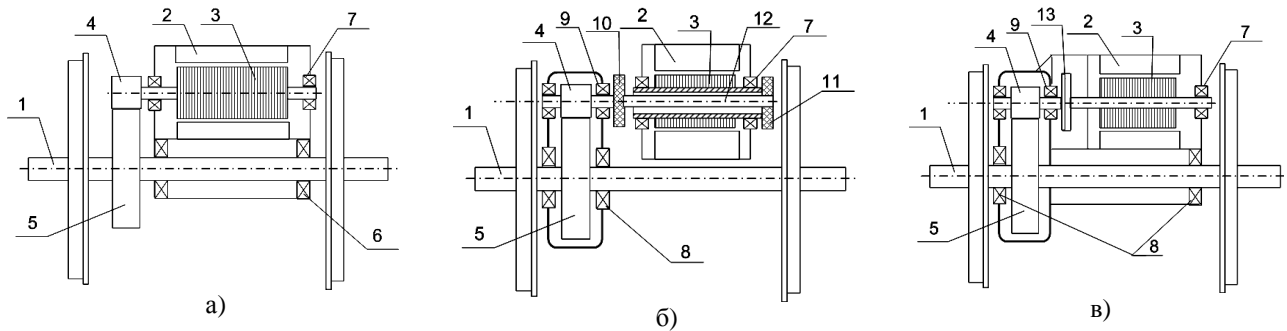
Варианты редукторного тягового привода: 1 – колесная пара; 2 – статор ТЭД; 3 – ротор ТЭД; 4 – малое зубчатое колесо; 5 – большое зубчатое колесо; 6 – моторно-осевой подшипник; 7 – подшипник ротора ТЭД; 8 – осевой подшипник редуктора; 9 – подшипник оси малого зубчатого колеса; 10, 11 – компенсирующие муфты; 12 – торсионный вал; 13 – дисковая муфта
